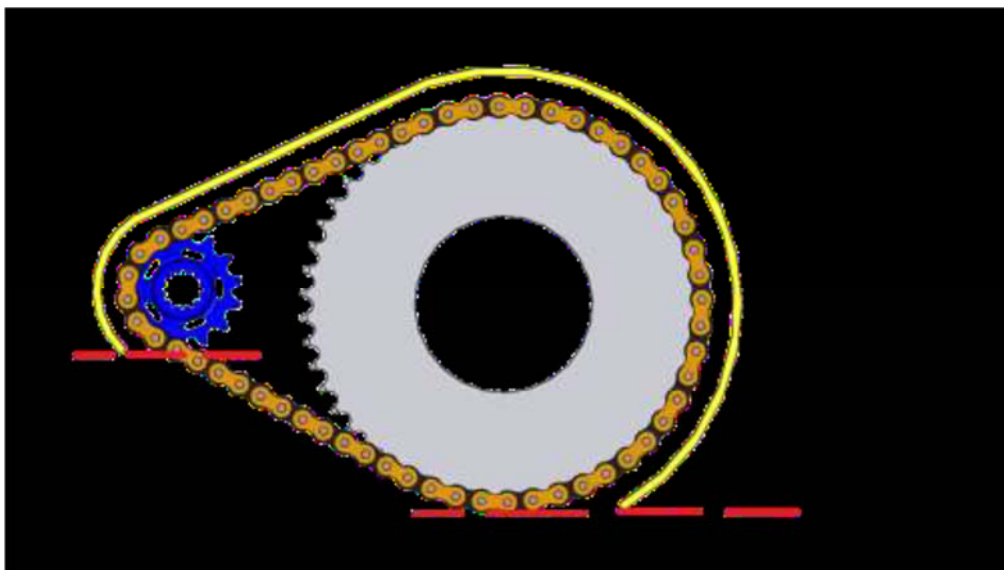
Detalle de cómo debe de fijarse la protección de la cadena.
